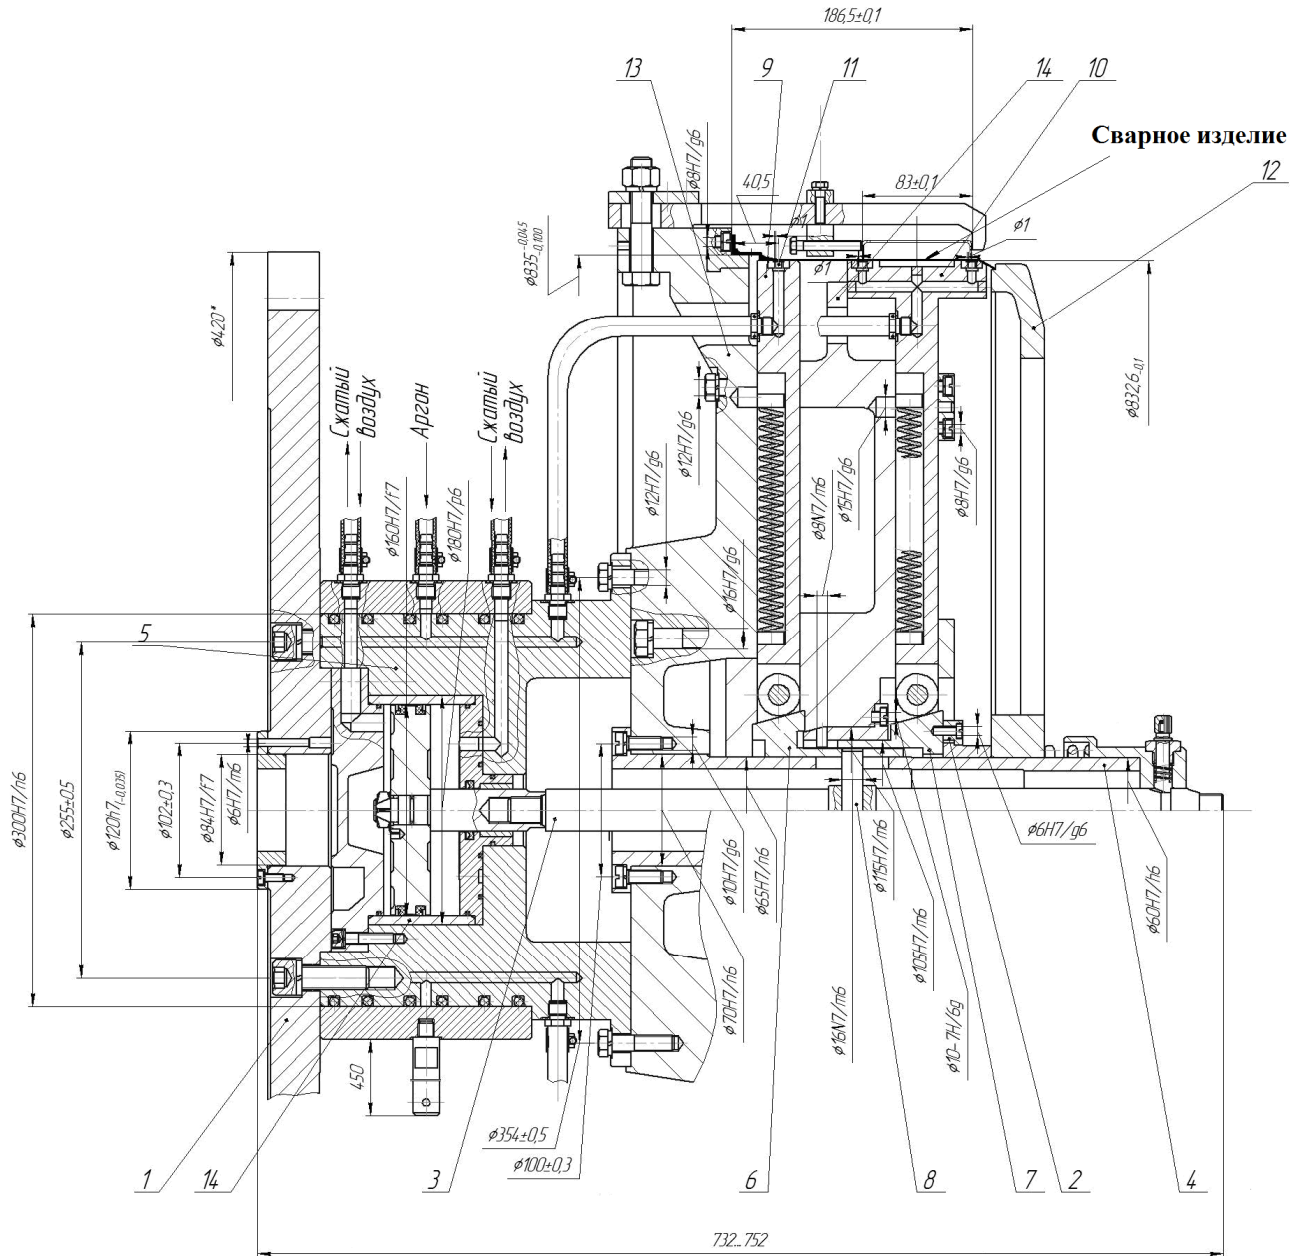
Приспособление для сварки кольцевого шва обечайки и фланца опоры турбины низкого давления двигателя АЛ-31Ф
